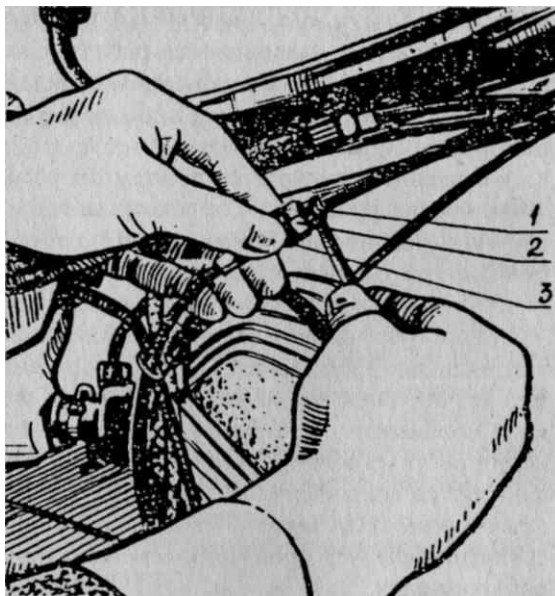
Регулировка свободного хода рычага выключения сцепления мокика с двигателем B50M: 1 — упор; 2 — контргайка; 3 — гайка регулировочная
